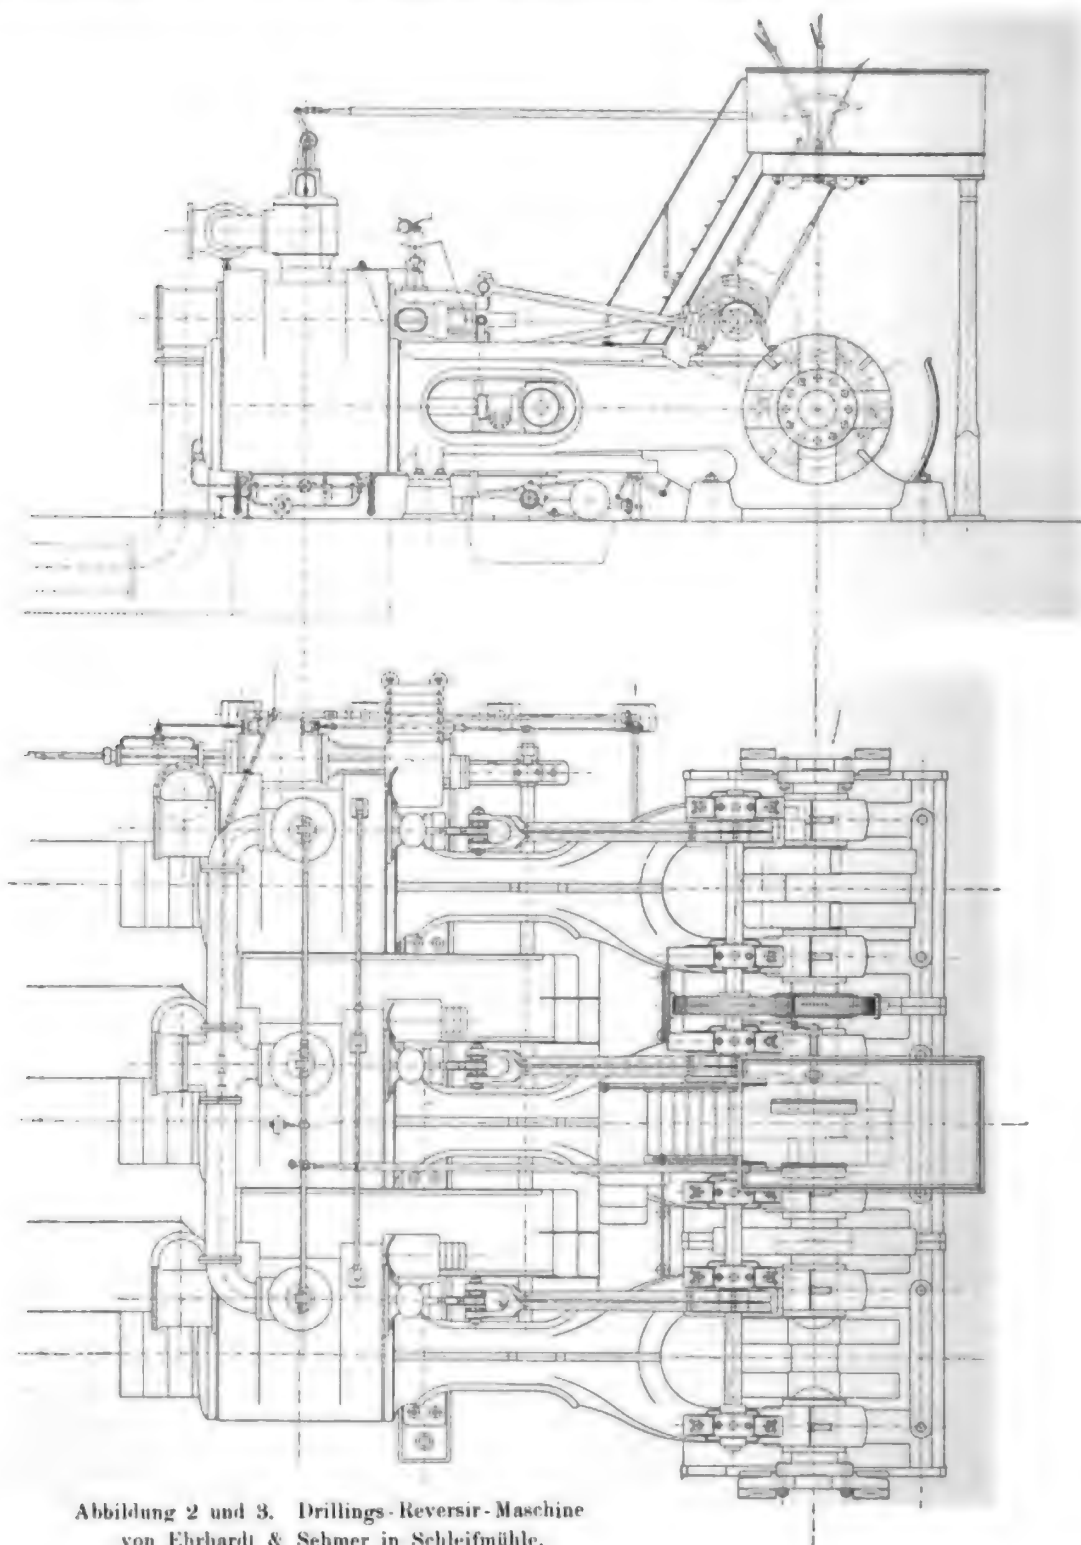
und 3. Drillings-Reversir-Maschine
